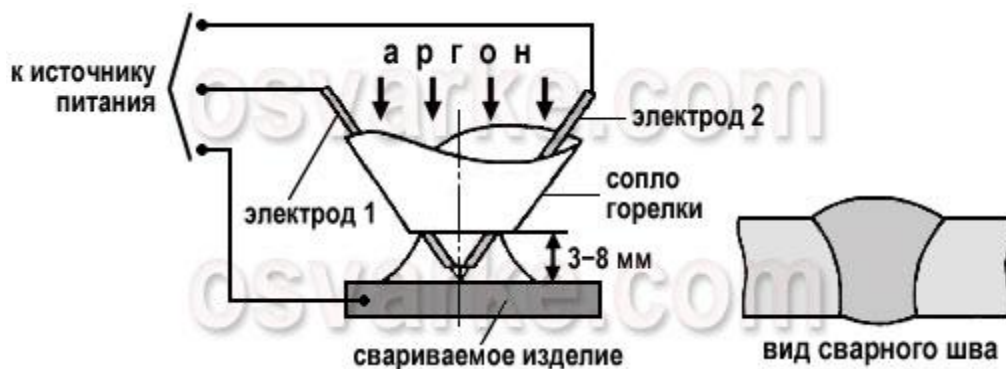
Схема сварки трёхфазной дугой
